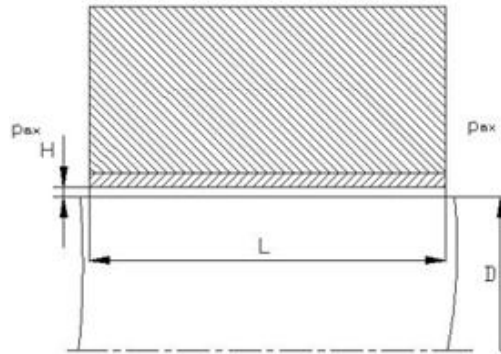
Конструктивна схема підшипника ковзання
